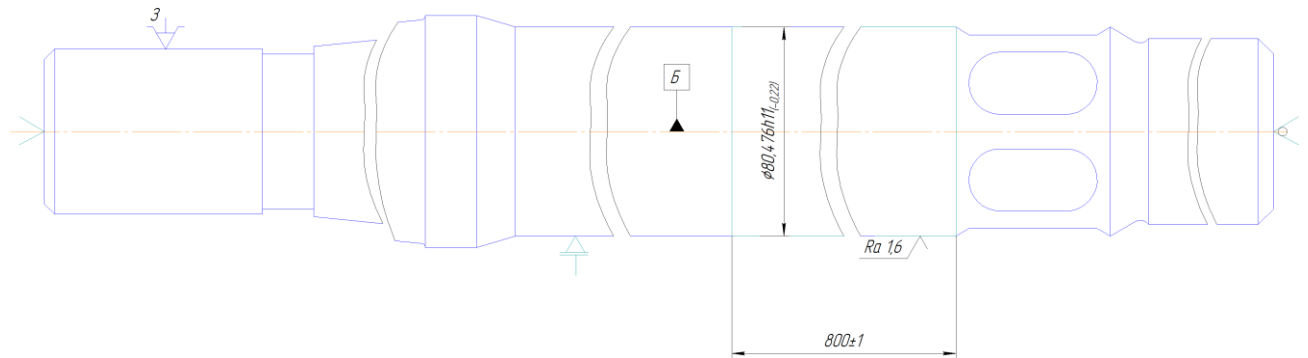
Ескіз на обробку поверхні 5 –  $\varnothing 80f9 \begin{pmatrix} 0,03 \\ 0,104 \end{pmatrix}$  штока БР.ПМ-17-037.00.001
